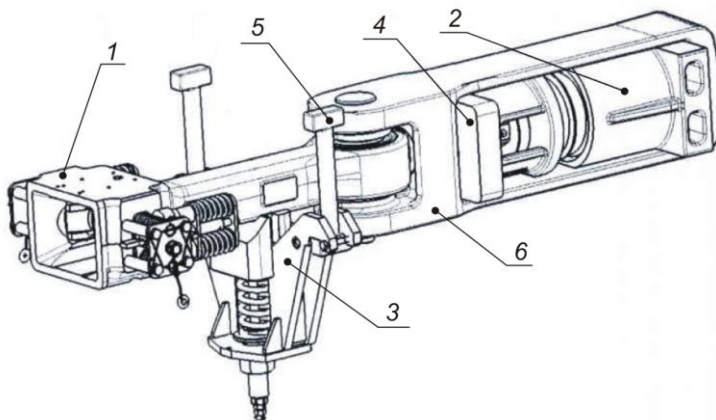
Общий вид сцепного устройства БСУ-ТМ136-13:
